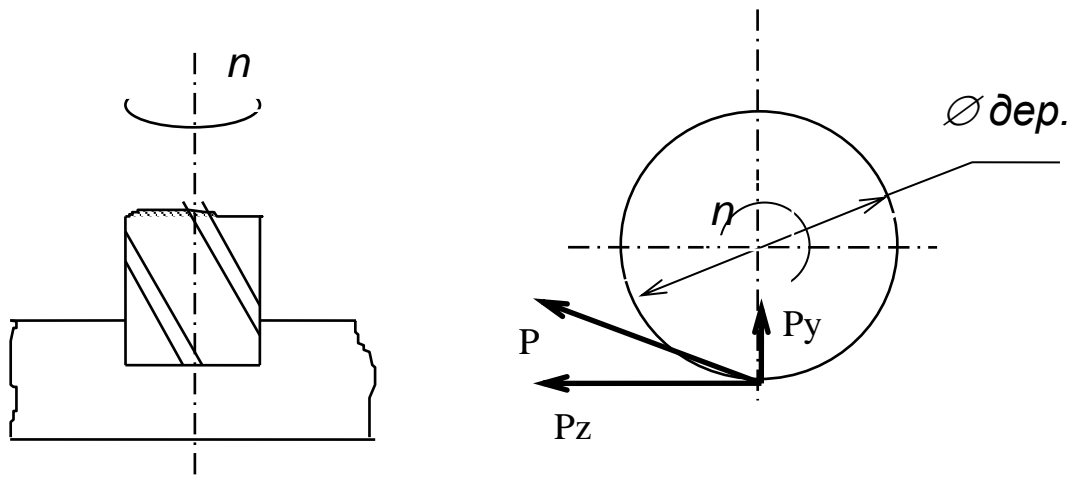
Схема фрезерування та діючі сили на фрезу
